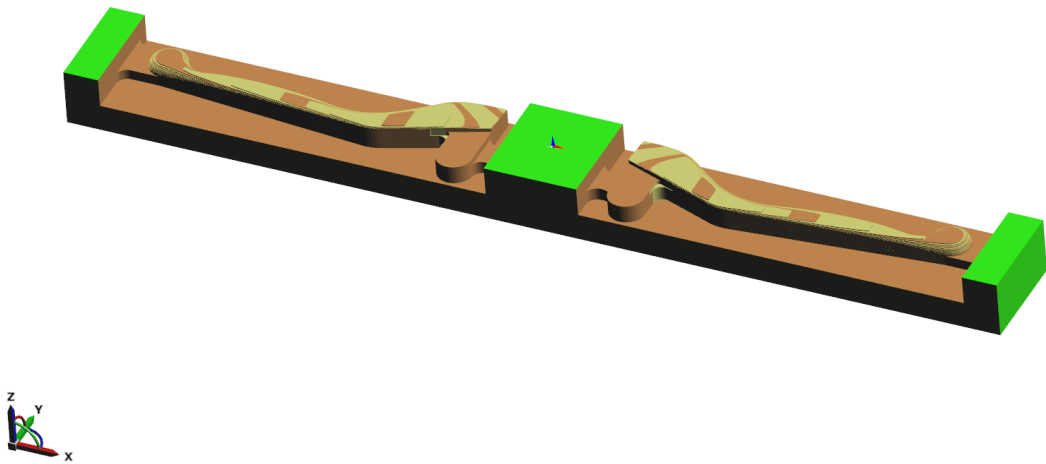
Brzdové páčky po hrubování v prvním upnutí
